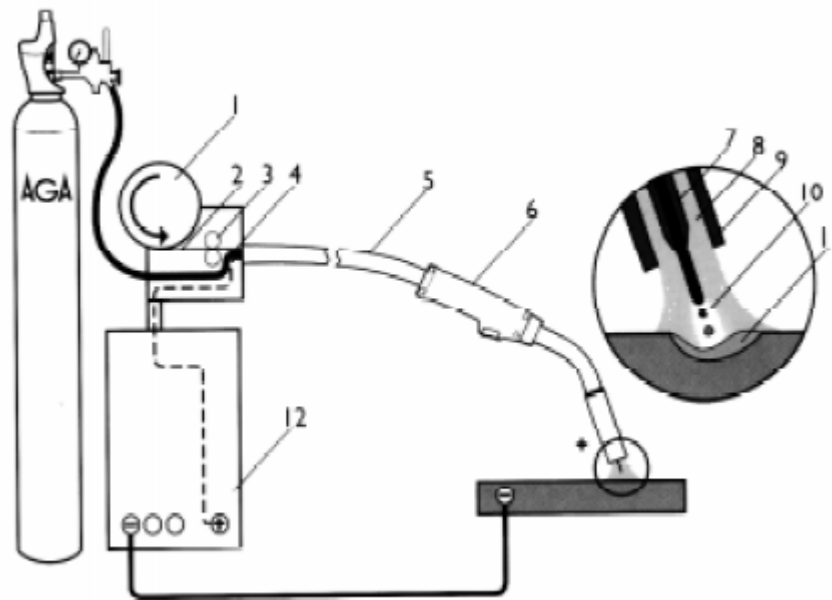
Partes de un equipo de soldadura MIG/MAG.
